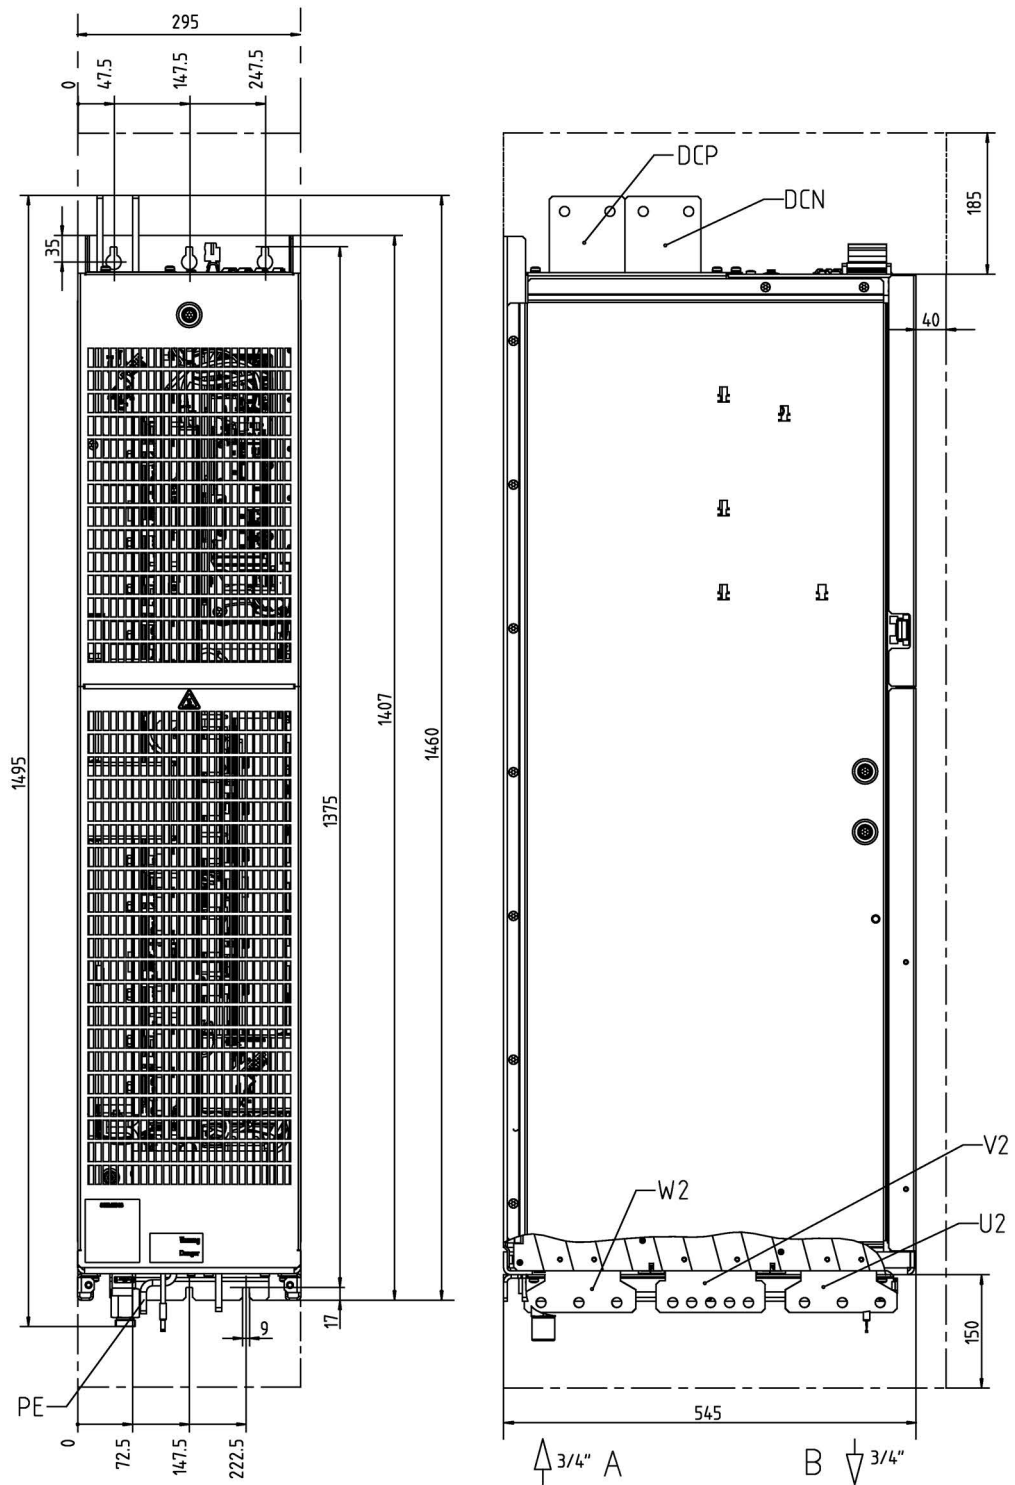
Габаритный чертёж модуля двигателя, типоразмер JXL, номер артикула 6SL3325-1TE41-4AS3, 6SL3325-1TG41-6AA3, 6SL3325-1TG41-6AP3. Вид спереди, вид сбоку
